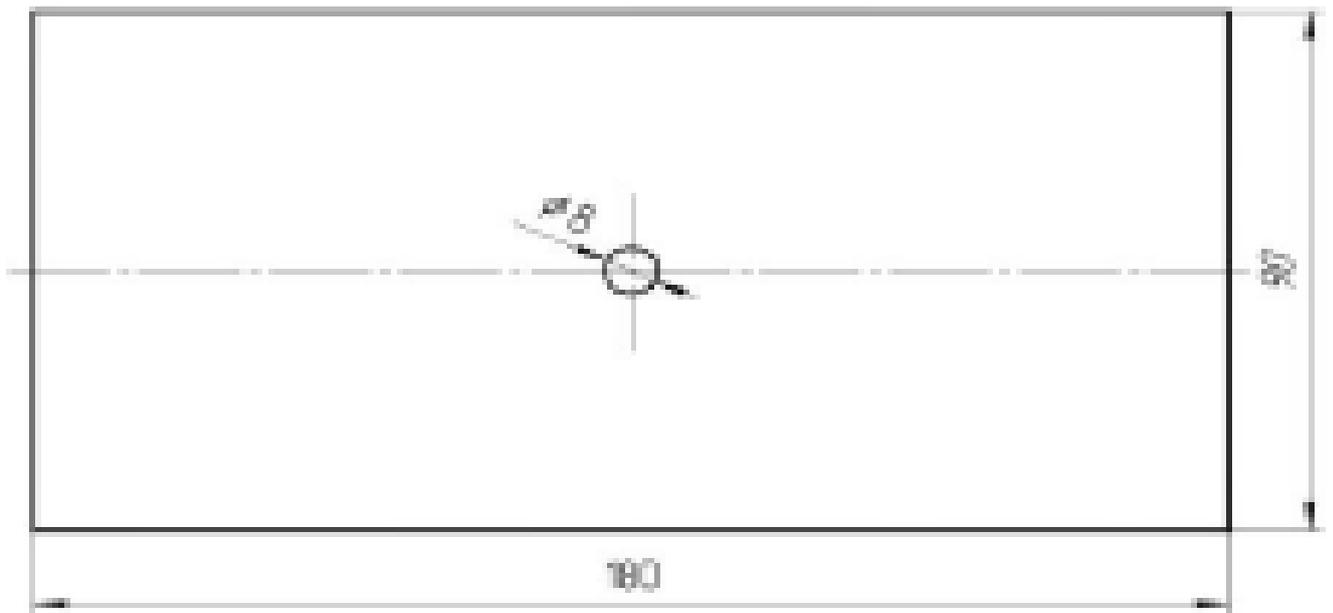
Фронтальное изображение корпуса приспособления для полировки
